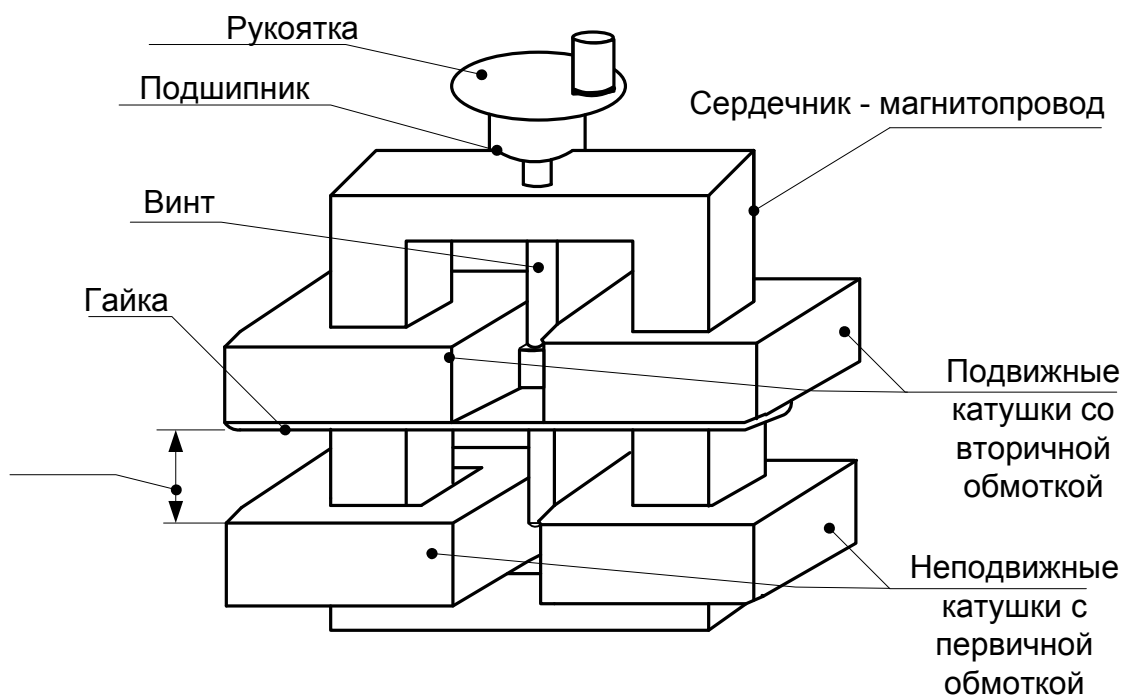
Конструктивная схема сварочного трансформатора с подвижными катушками вторичной обмотки
